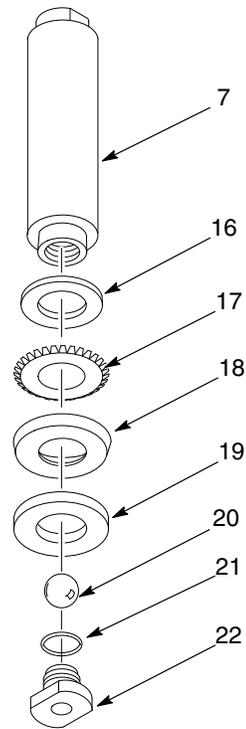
Reparieren der Baugruppe Tauchkolben
